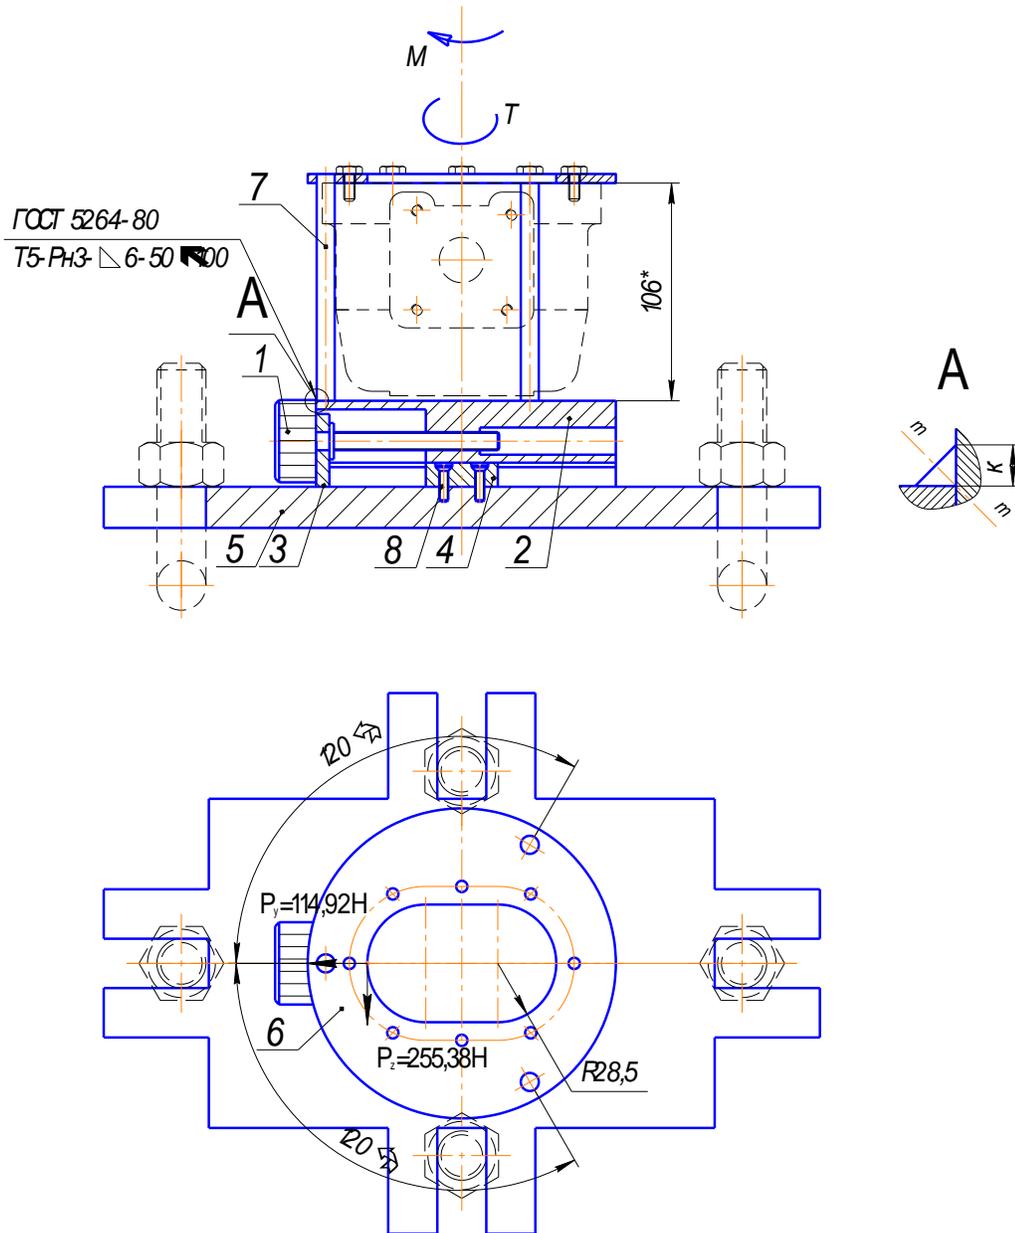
Расчетная схема сил, действующих на сварное соединение:
